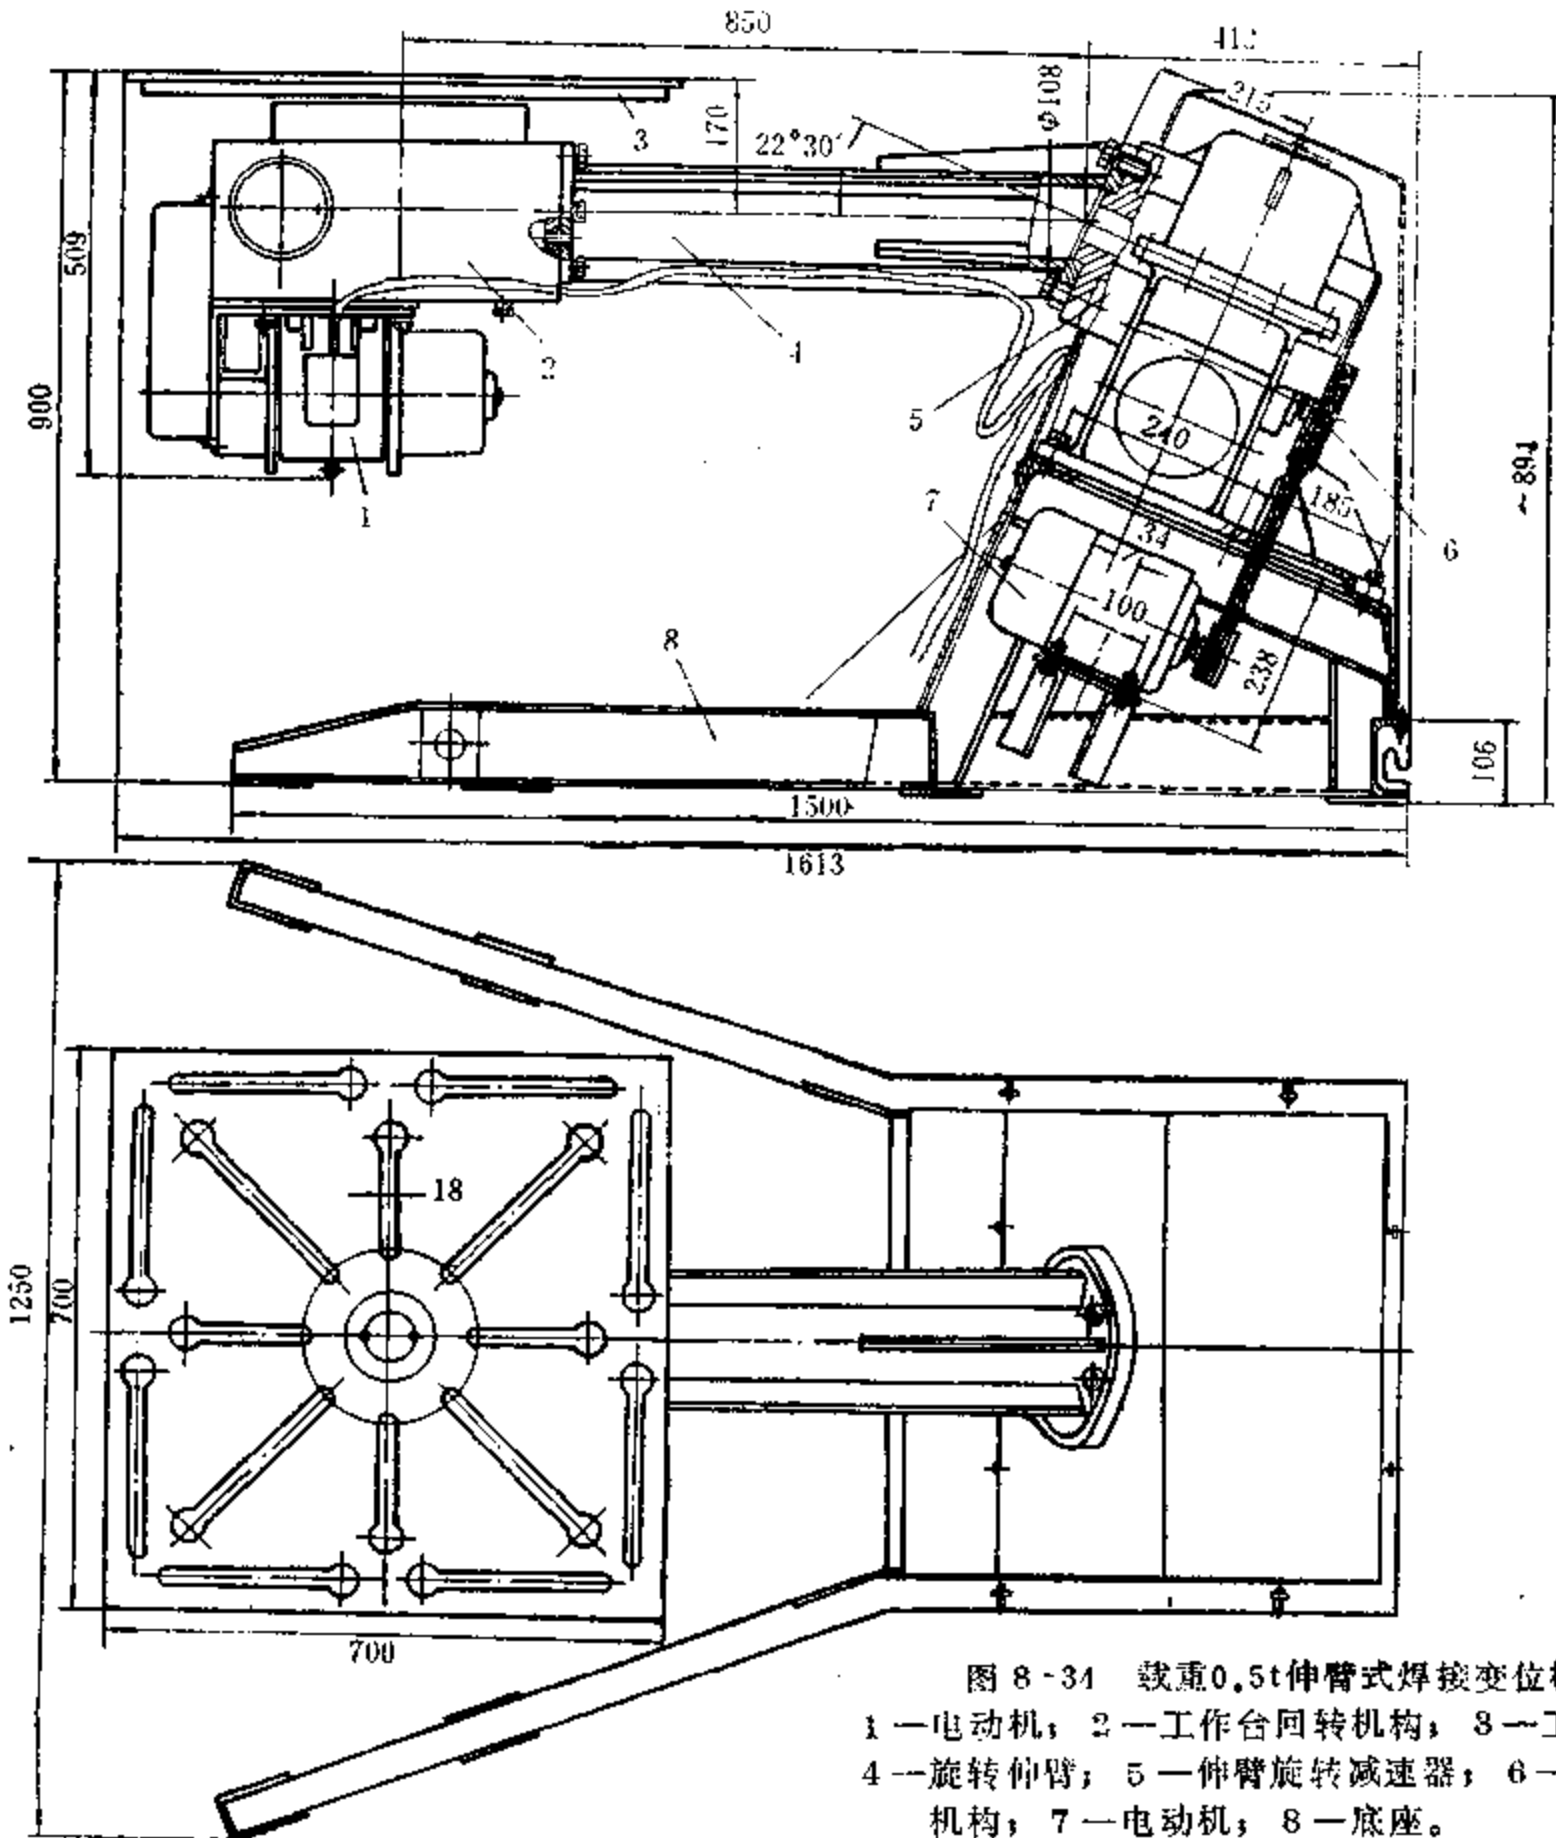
载重 0.5t 伸臂式焊接变位机
